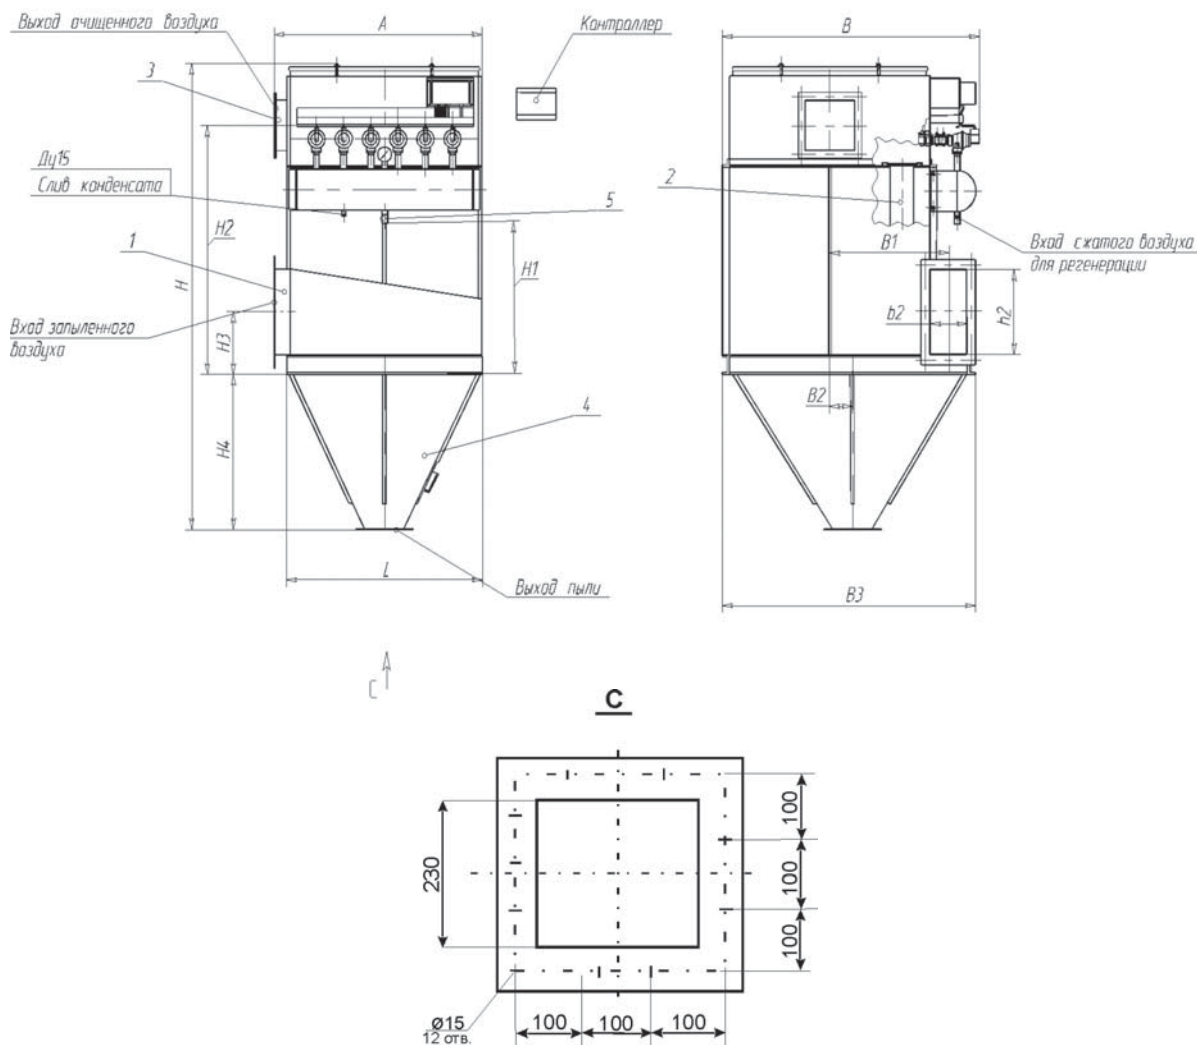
Схема фильтров рукавных типа FRIP-5; FRIP-10; FRIP-15; FRIP-30; FRIP-180.
